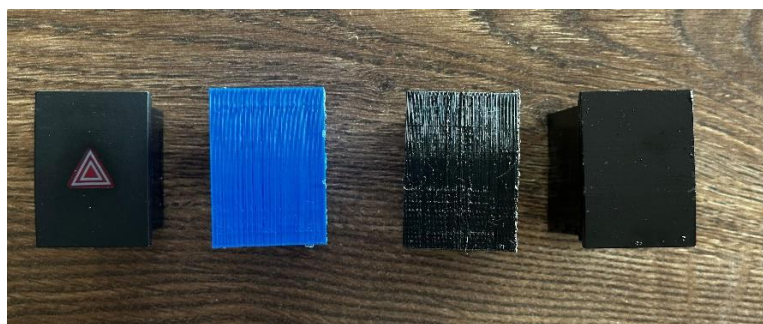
Fabricación tradicional – PLA – PETG – Resina (Botón de Parqueo)
